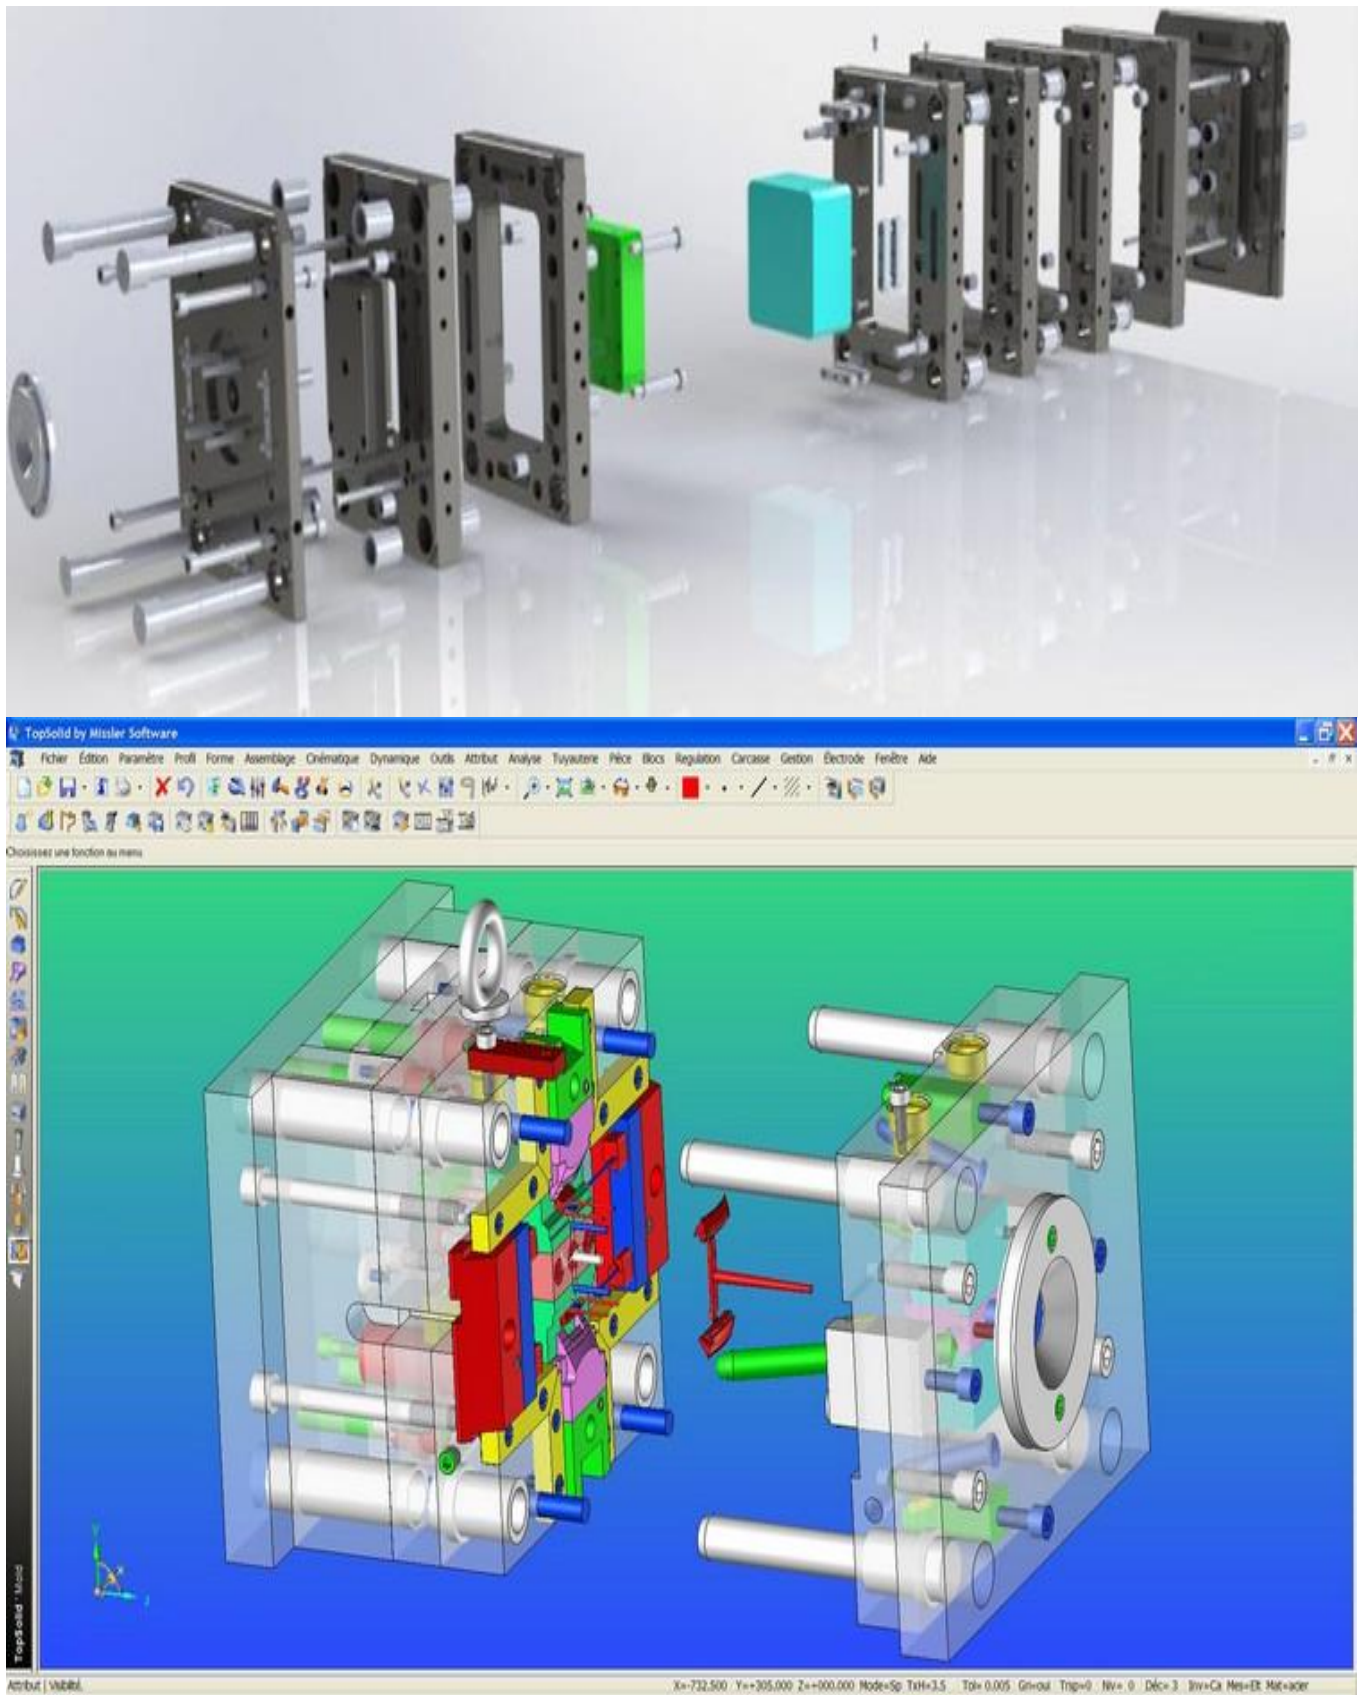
Vue éclaté d'un : Moule à injection plastiques
